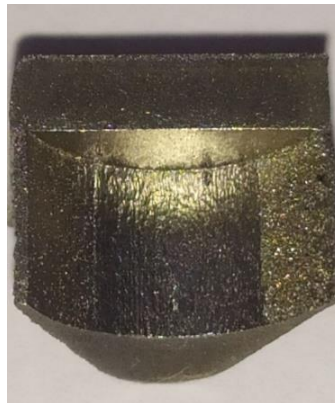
Загальний вигляд закритої робочої поверхні лопатки.
